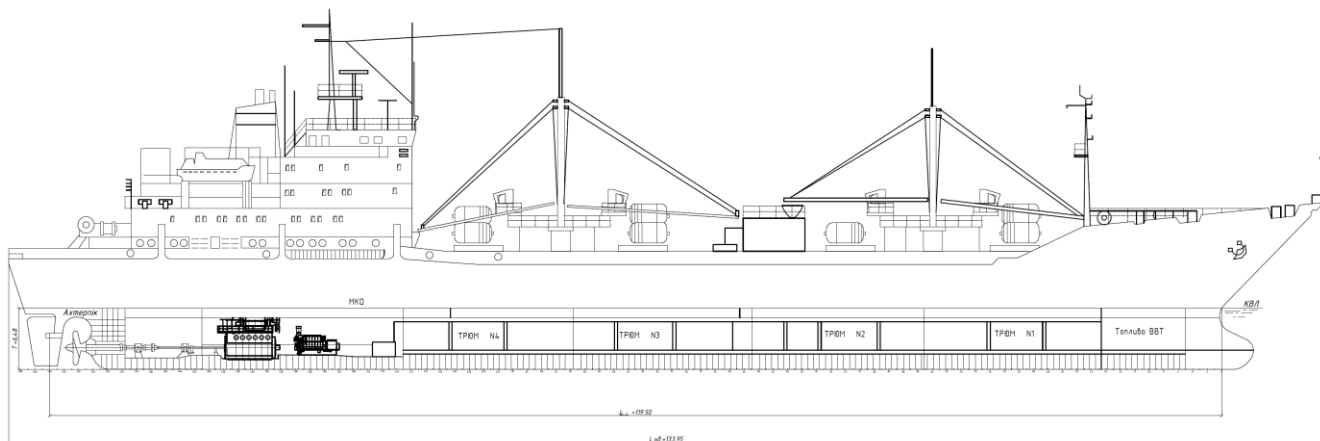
Загальний вигляд транспортного рефрижератора
